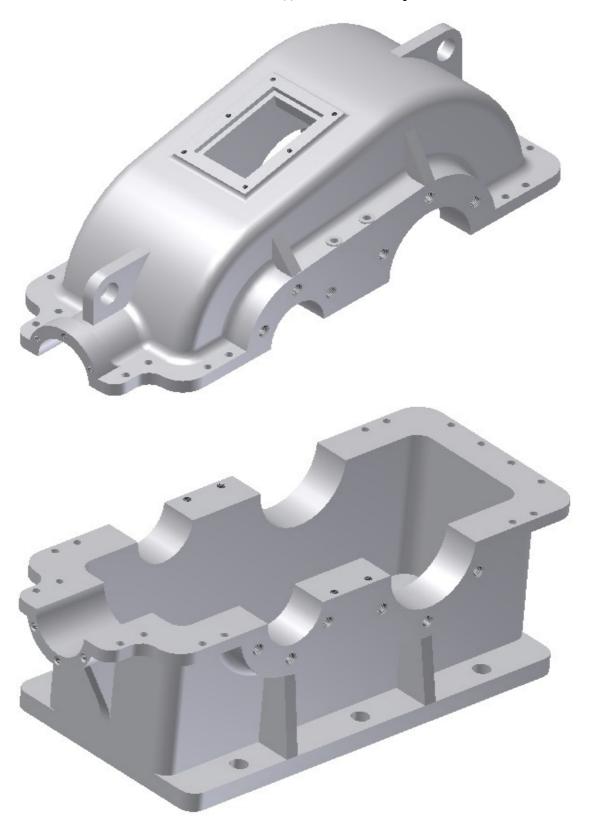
Трехмерные модели крышки и корпуса редуктора
